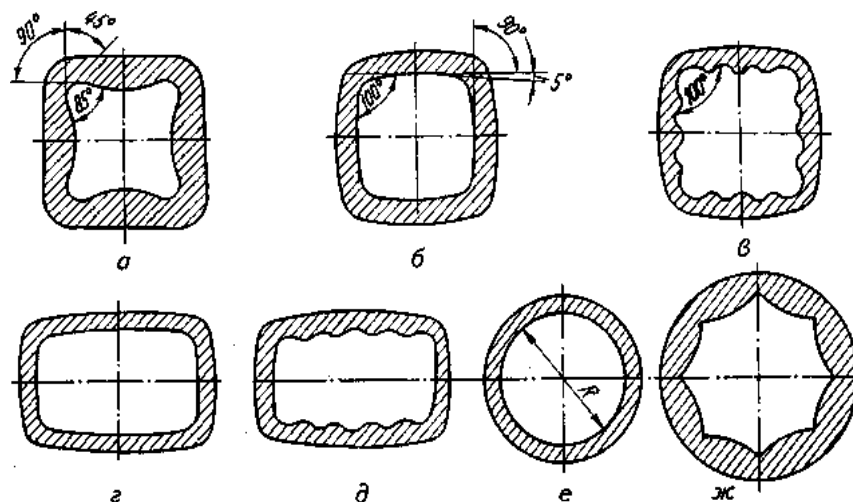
Форми (а–ж) поперечного перетину виливниць
